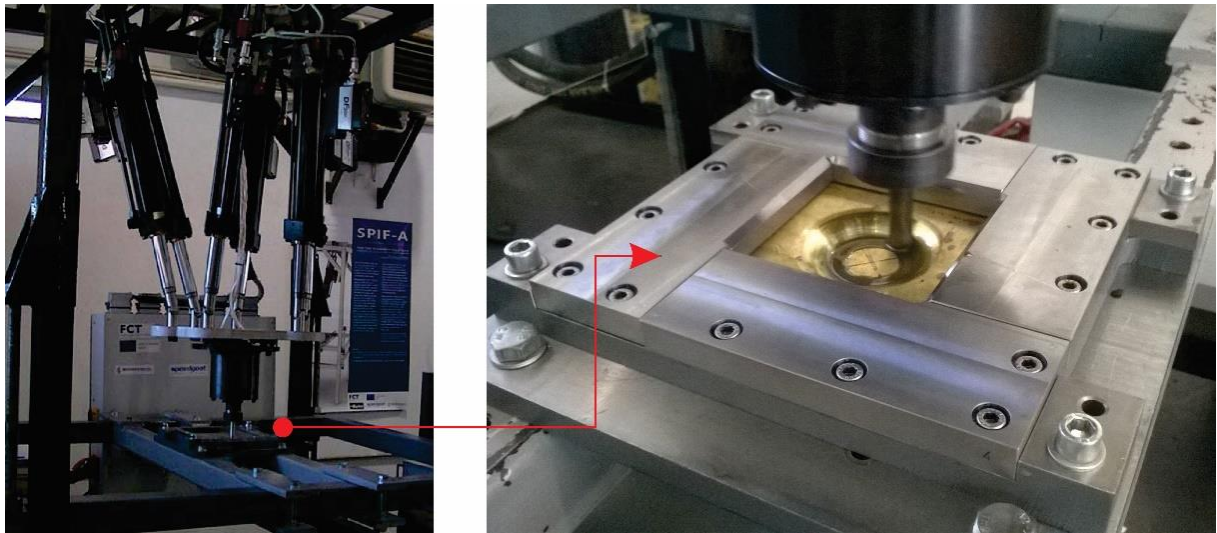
Processo SPIF: a) Máquina Dedicada – SPIF-A; b) Matriz de Estampagem
